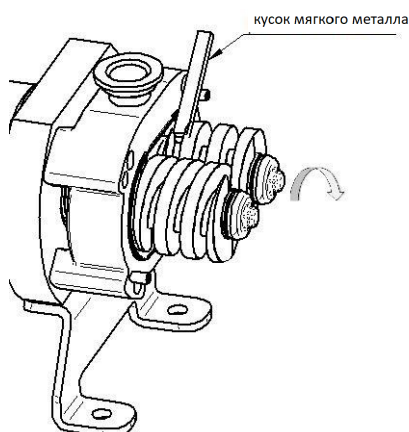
сборка винта, вращающегося по часовой стрелки.
